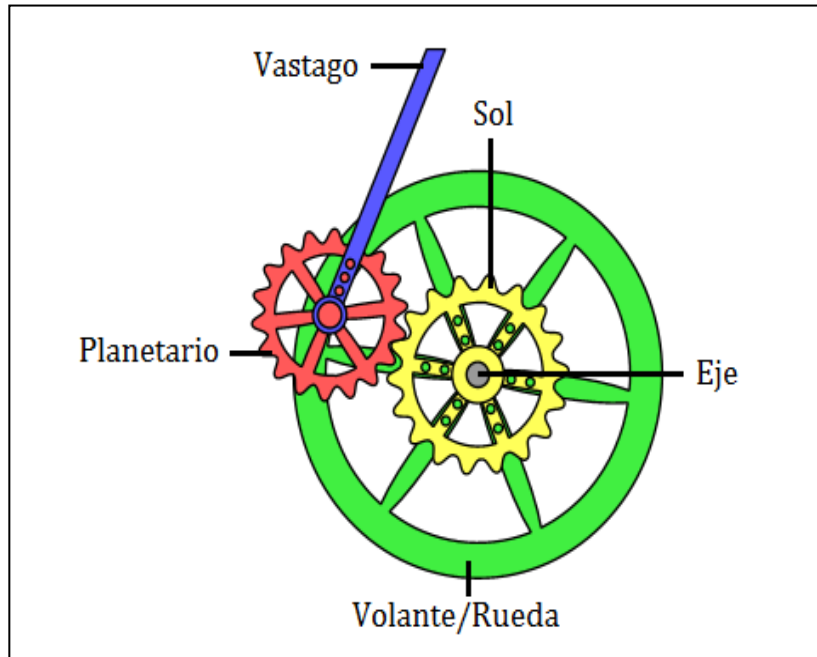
Engranajes de Sol y Planetas⁷⁵
